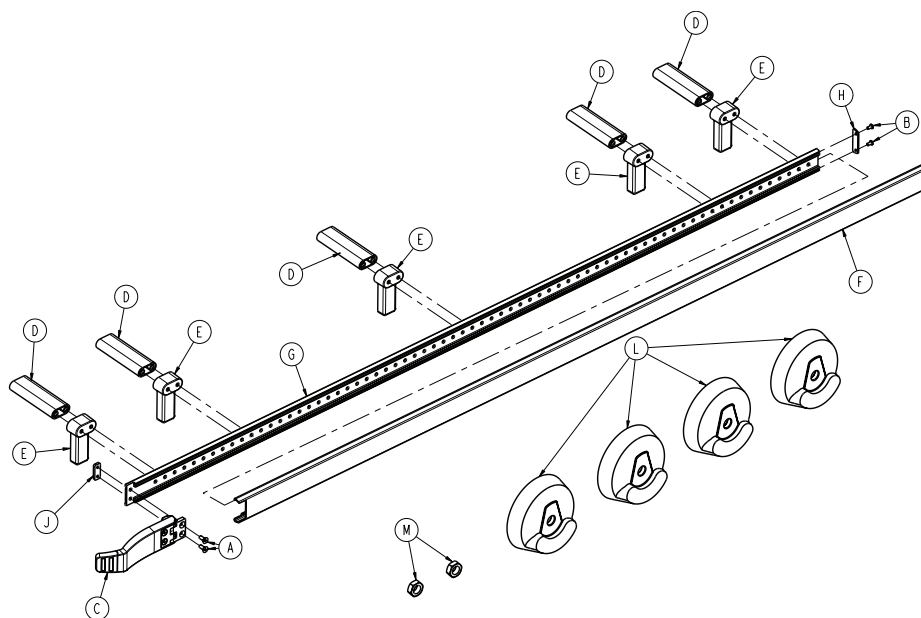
Необязательные компоненты комплекта направляющей для колес — 6390-027-000
